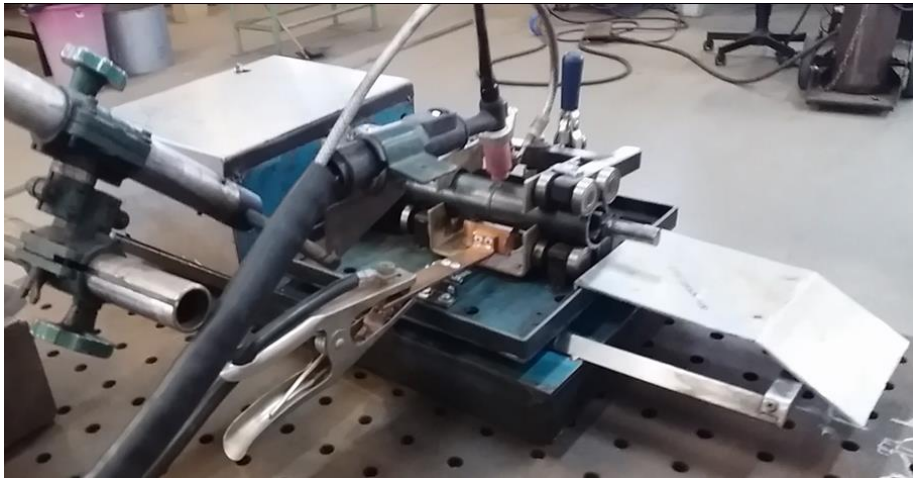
Modelo mecânico rotativo para controle do processo de corte e soldagem de tubos redondos, (Coelho F., Gonçalves G.M.B., 2018)
